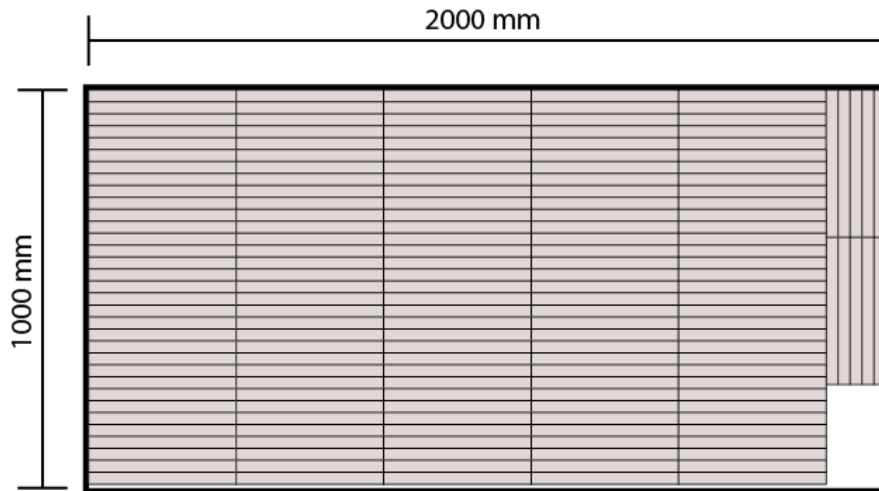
Cortes de las piezas “soporte de agarre del separador” en una plancha de grilon
